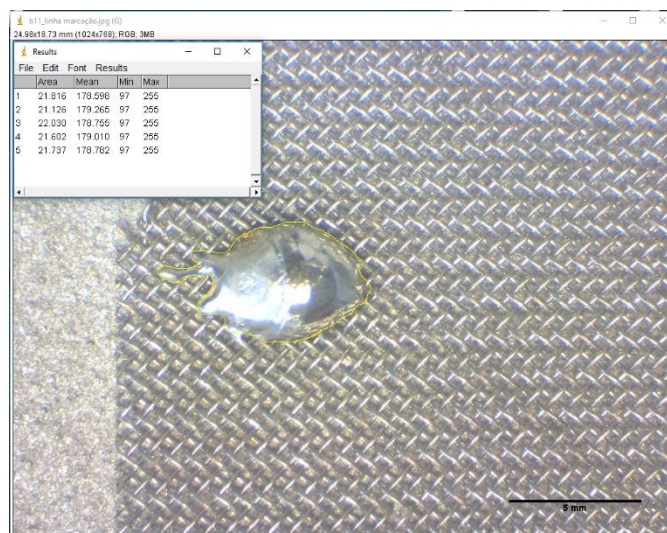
Determinação das Áreas de Soldadura dos Provetes Ligados Segundo o Processo de Brasagem Fraca.
